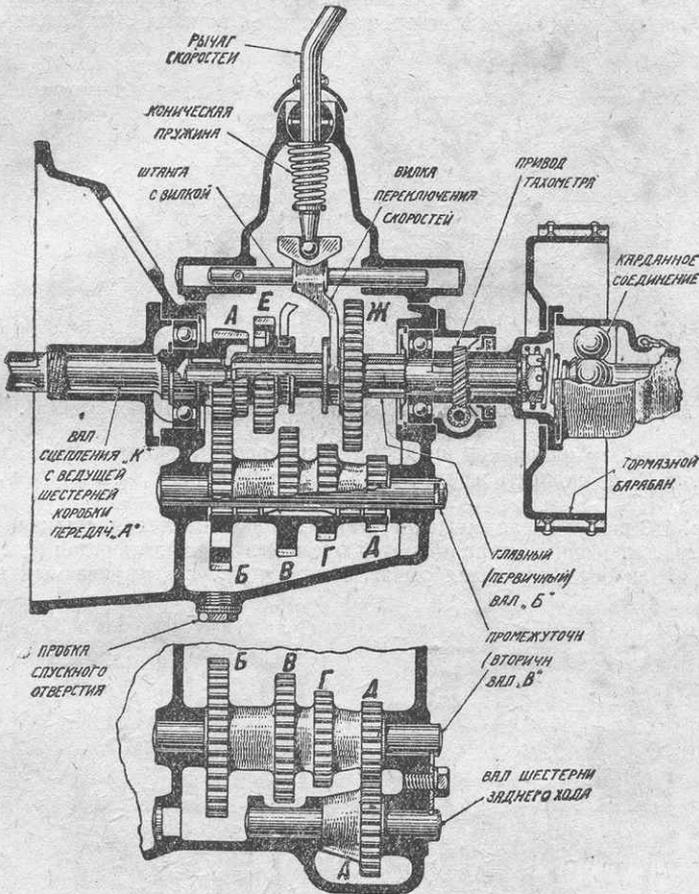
Трехскоростная коробка передач с качающимся рычагом скоростей.
